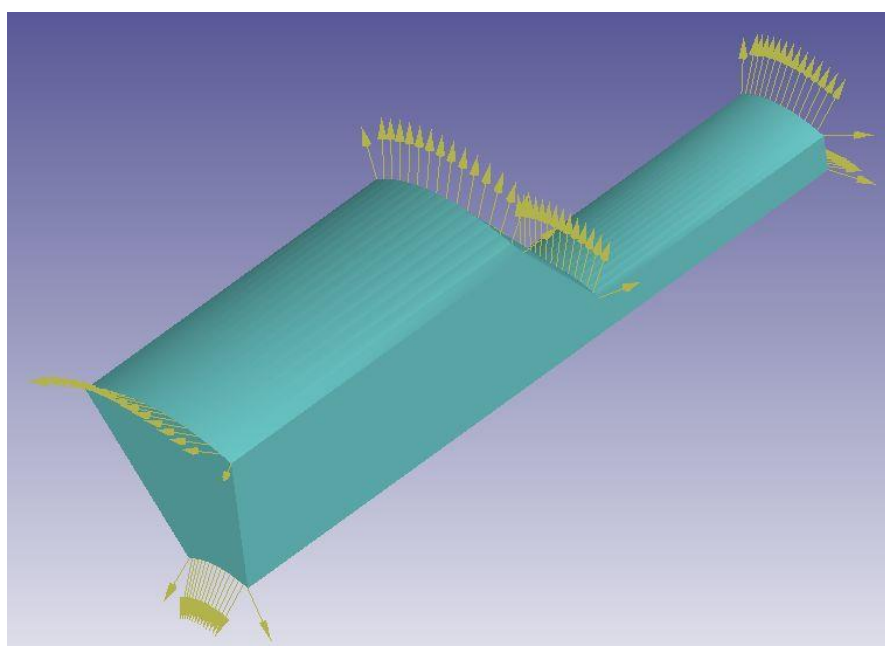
Установленное расположение нормалей к поверхности заготовки
